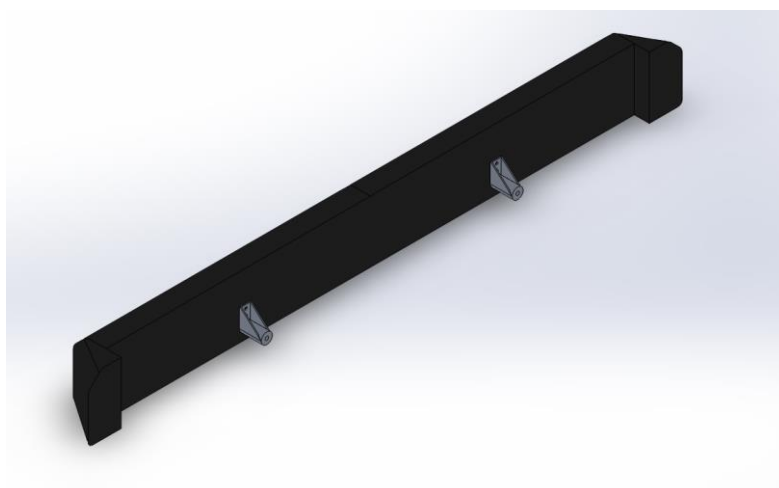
kit montaje carenado trasero. Fuente: propia.
